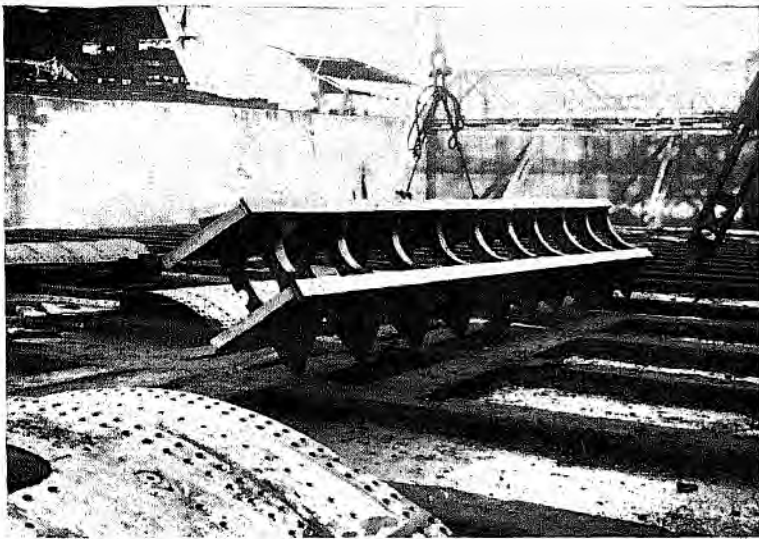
DE GEHEEL GELASCHTE FUNDATIE VOOR DE DIESELMACHINES
